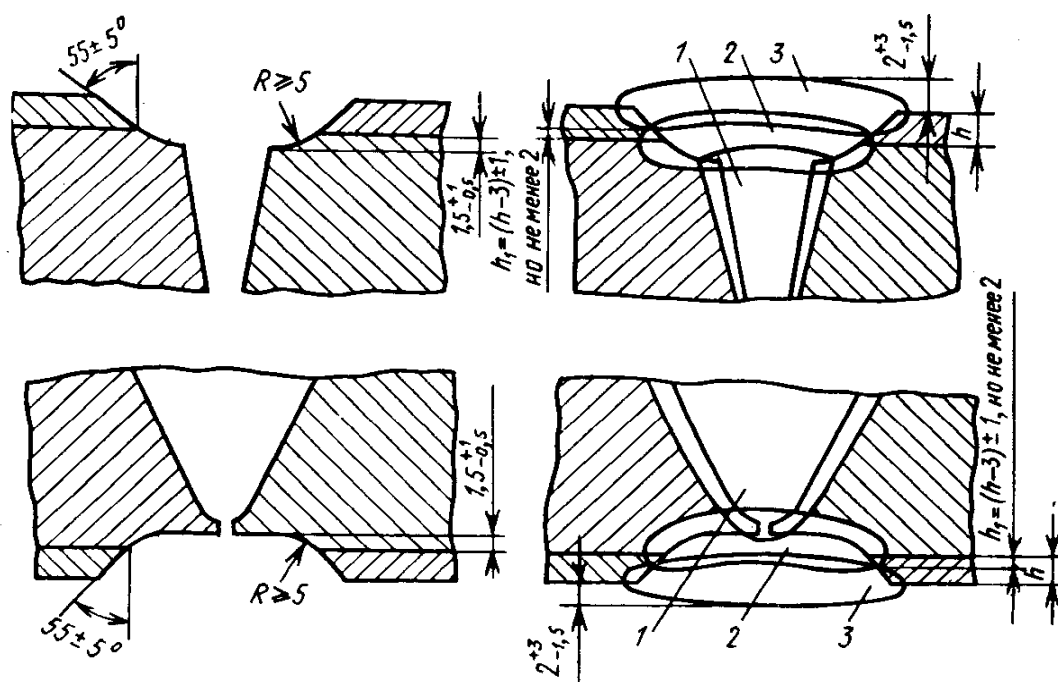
Схема разделки и выполнения сварных соединений деталей из двухслойных сталей:
